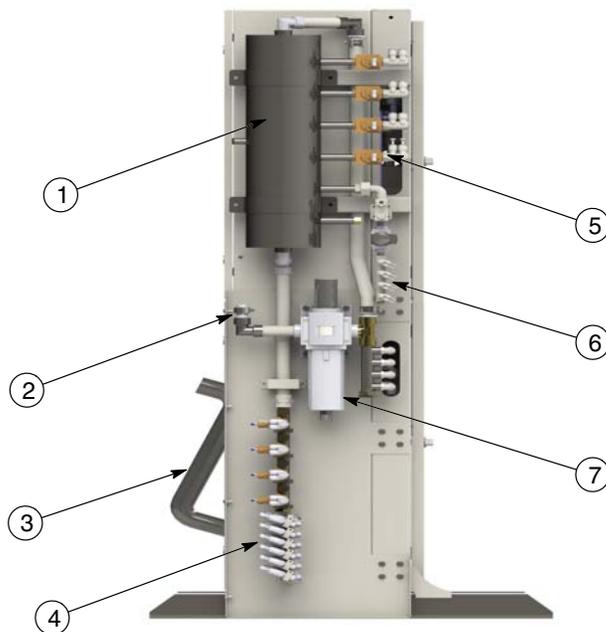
Vue d'ensemble des principaux composants pneumatiques
